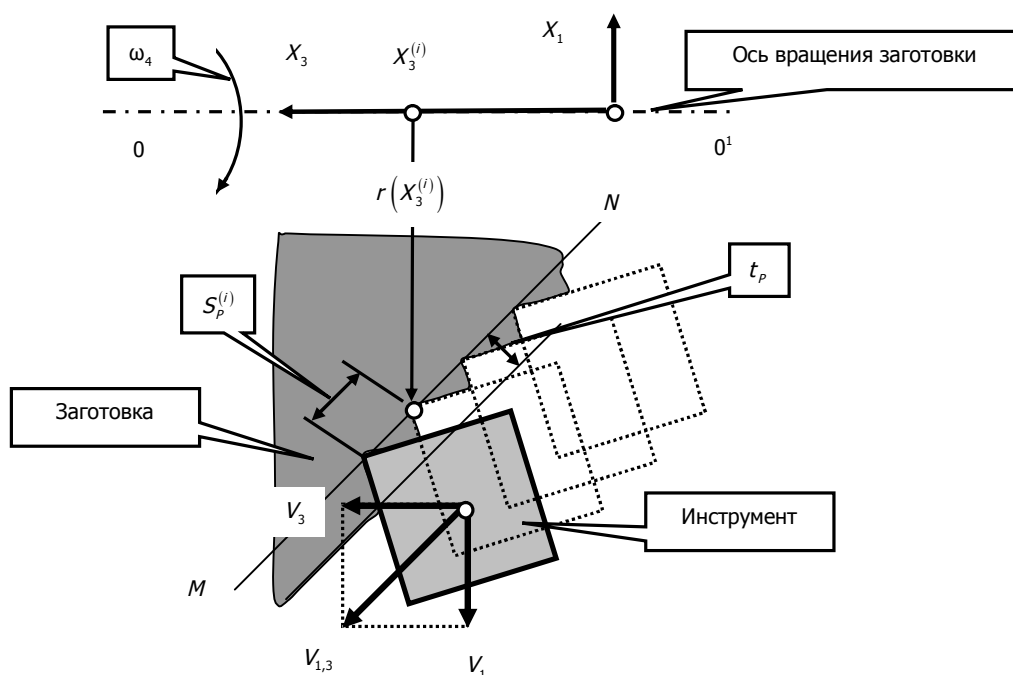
Схема формирования формообразующих движений при точении детали сложной геометрической формы
